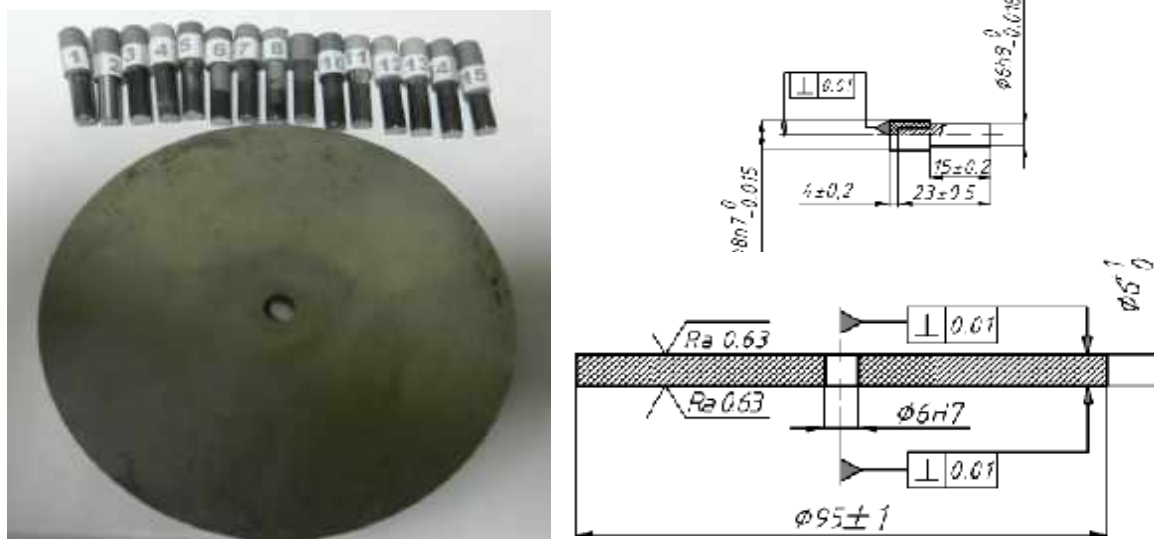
Imaginea și dimensiunile epruvetelor pentru testele PIN-la-disc
